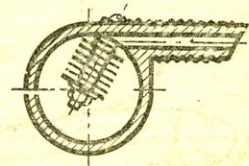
Схема монтажа ламельного глушителя в объеме глушителя двигателя «Талка-7».
